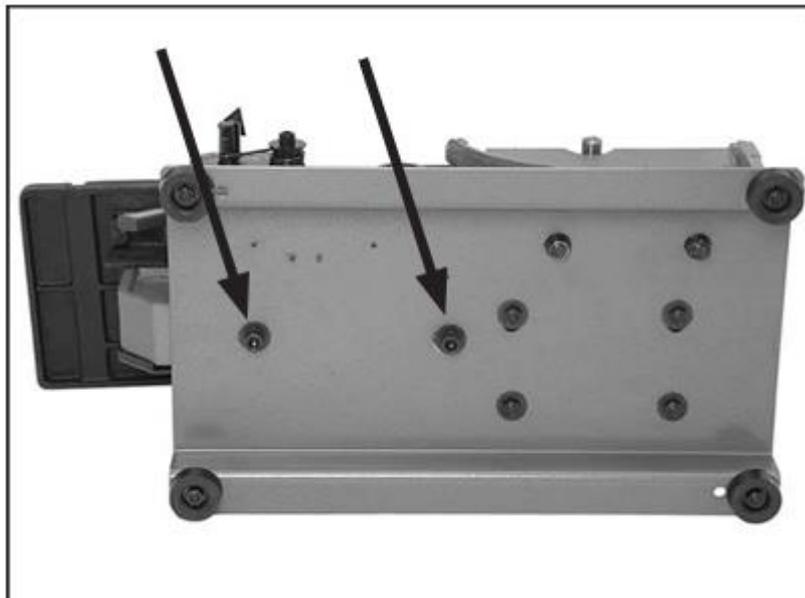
Винты с заглушками, которыми крепится корпус ремня (если смотреть снизу основания).
